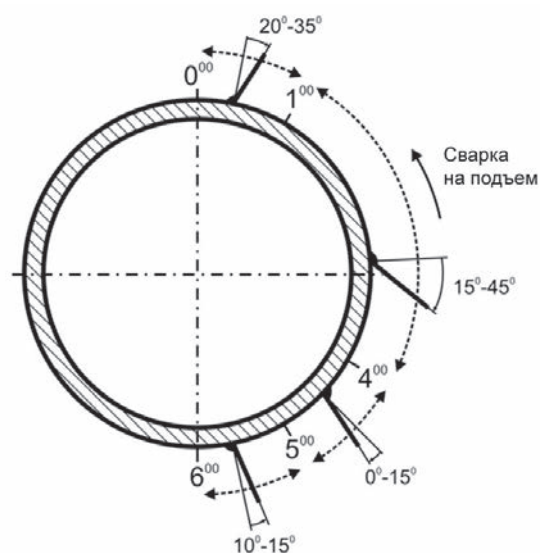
Схема расположения сварочной горелки при механизированной дуговой сварке в различных пространственных положениях заполняющих и облицовочных слоев
